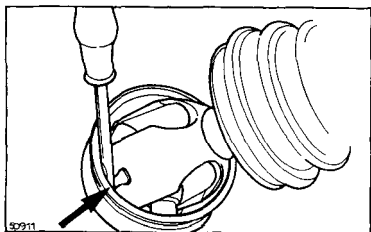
Установка пластин держателя в пазах вилки шарнира
